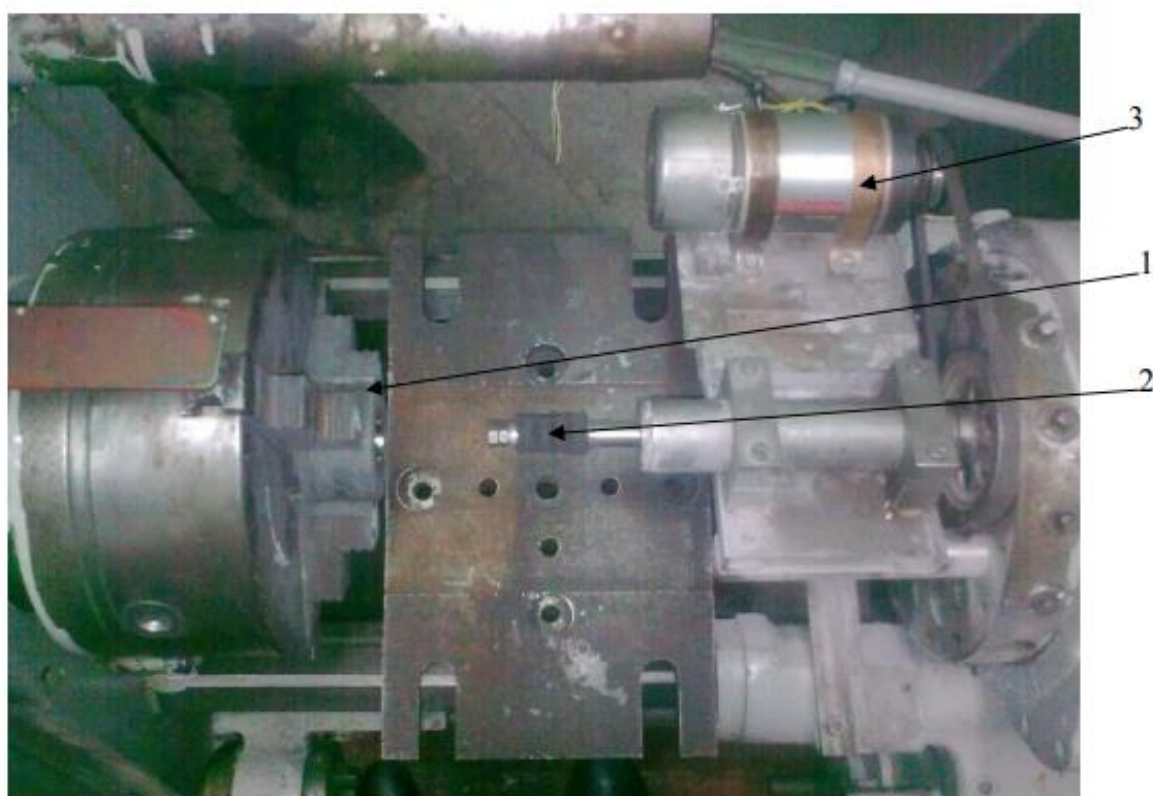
Вид зверху на експериментальну установку для МАО внутрішніх поверхонь на базі токарно-револьверного верстата 1341: 1- заготовка; 2 - оправка з магнітними кільцями; 3 – привід
